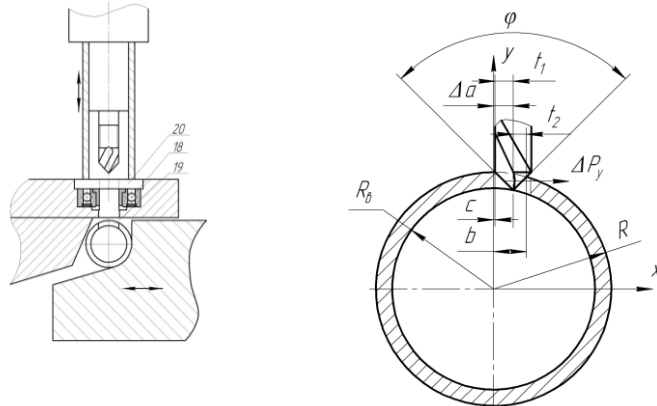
Розрахункова схема для визначення величини невірноваженої радіальної сили на свердлі
